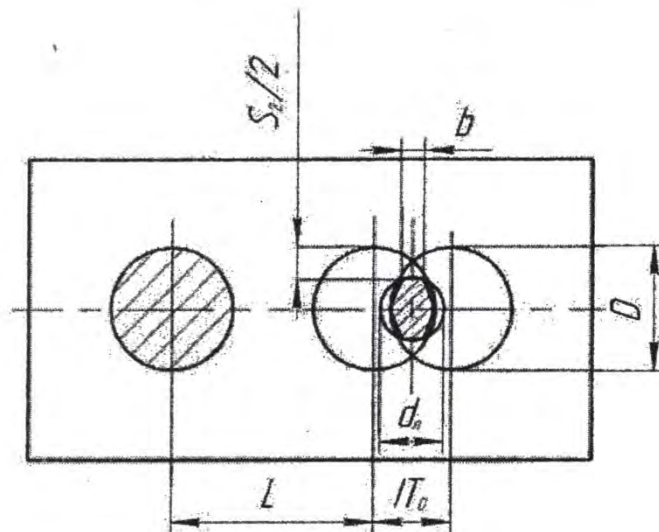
Схема установки заготовки на один цилиндрический и один срезанный пальцы
